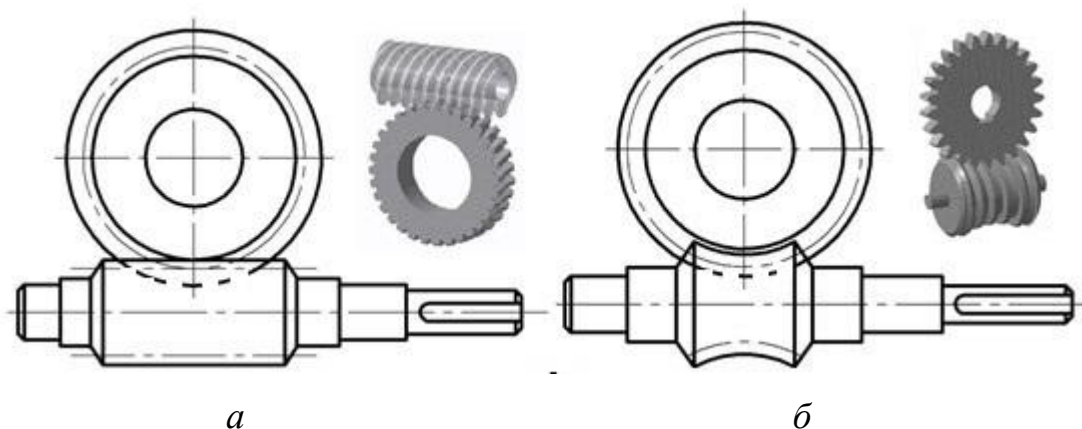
Форми зовнішньої поверхні черв'яка
